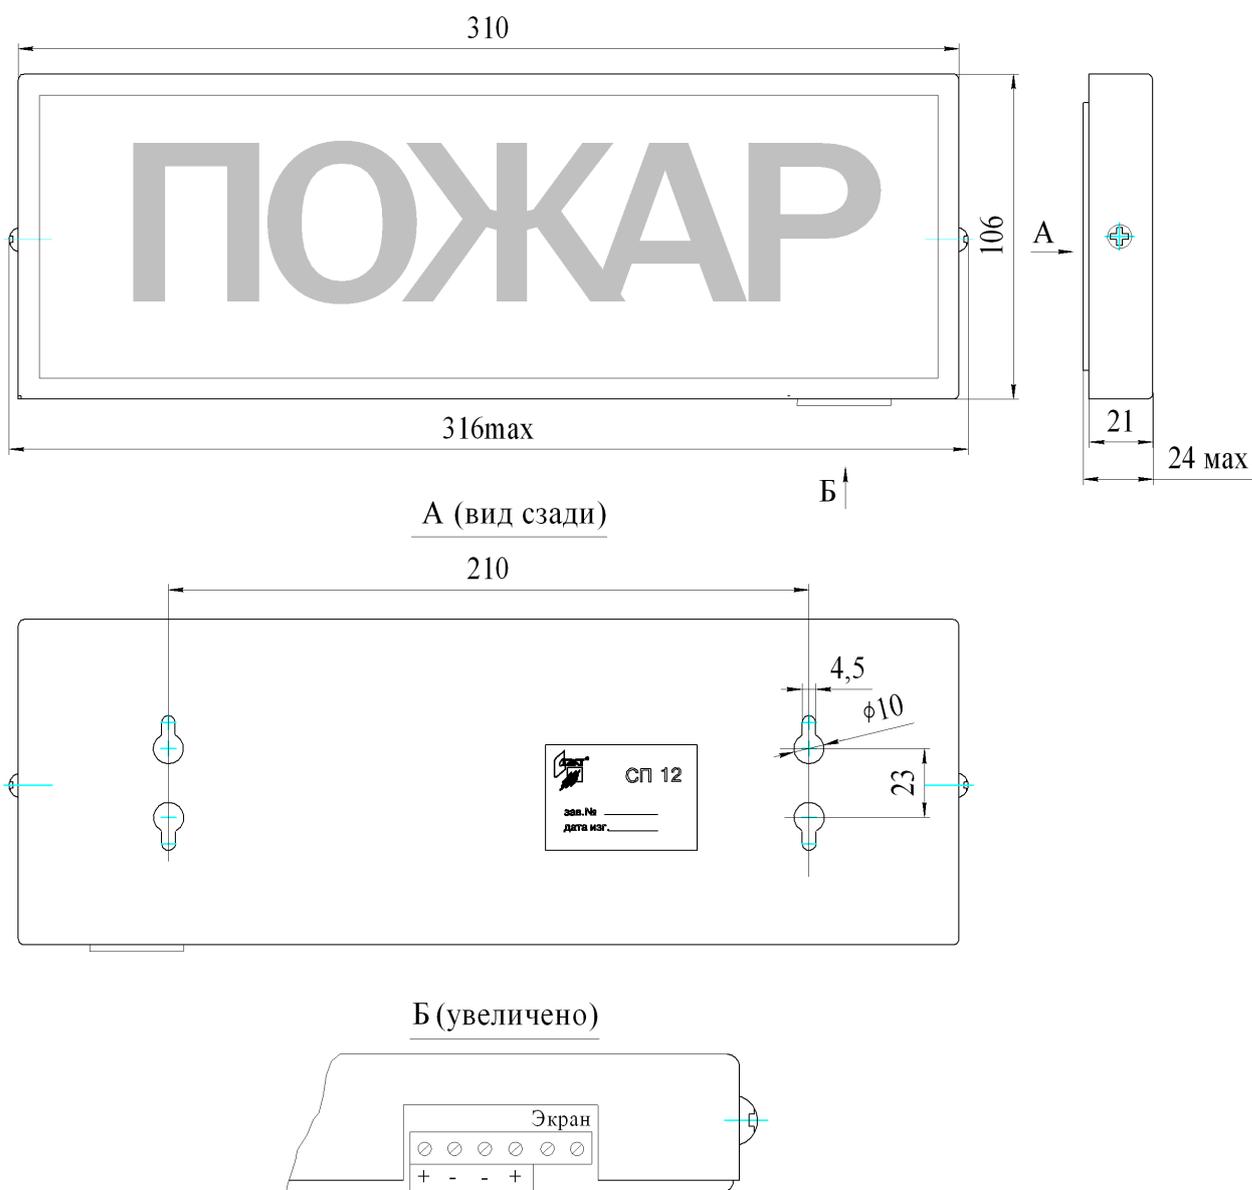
Оповещатель СП 12. Габаритный чертёж
